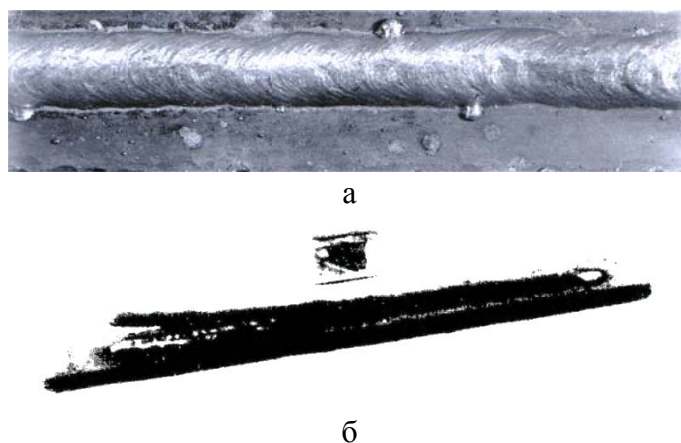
Внешний вид наплавленного валика (а) и шлаковой корки (б) при наплавке порошковой проволоки
